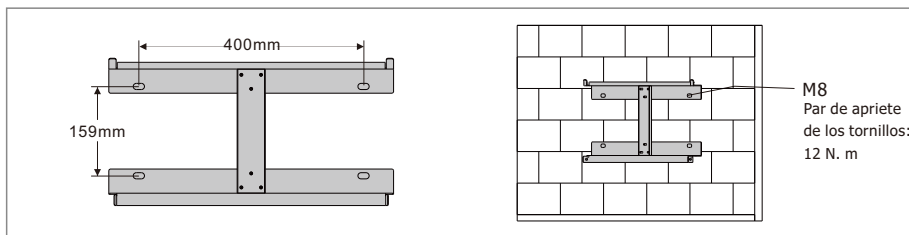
Instalación de la placa de suspensión del inversor
